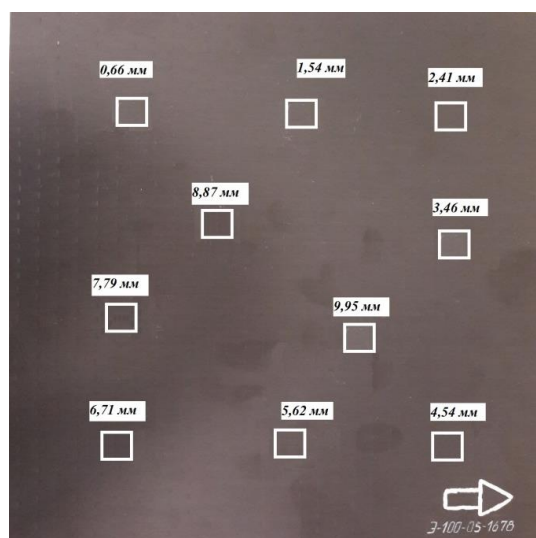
Внешний вид образца с внедренными имитаторами дефектов
